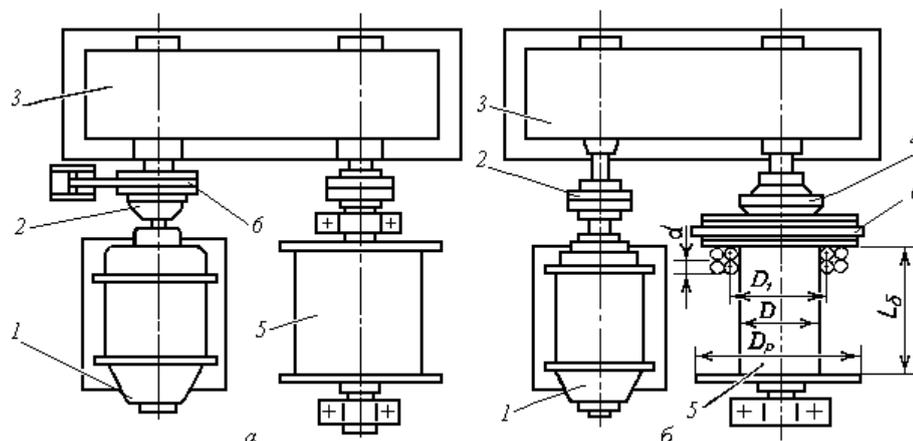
Типы лебедок: а – подъемная; б – транспортная; 1 – двигатель; 2 – муфта соединительная; 3 – редуктор; 4 – муфта включения; 5 – барабан; 6 – тормоз
